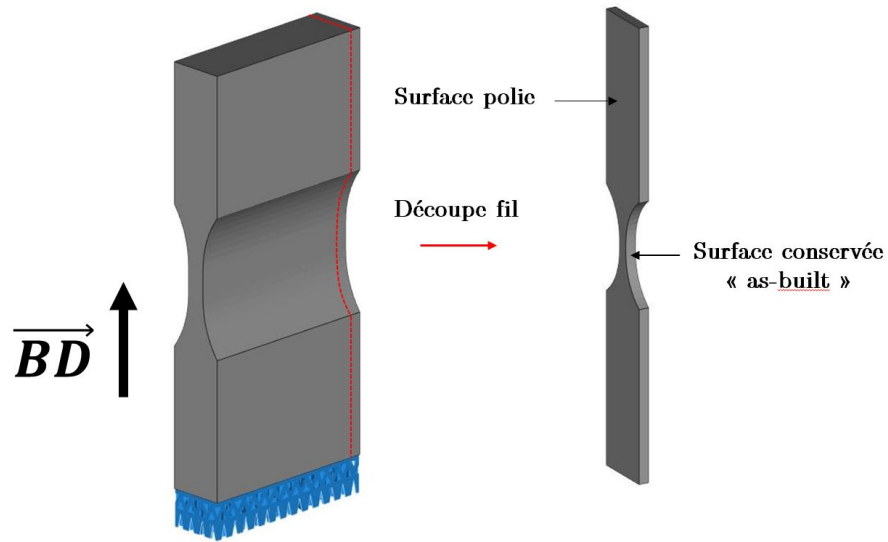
Procédé d'obtention des éprouvettes plates
